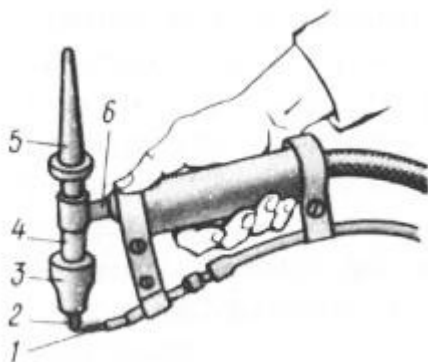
Горелка для аргонно-дуговой сварки не плавящимся электродом:
